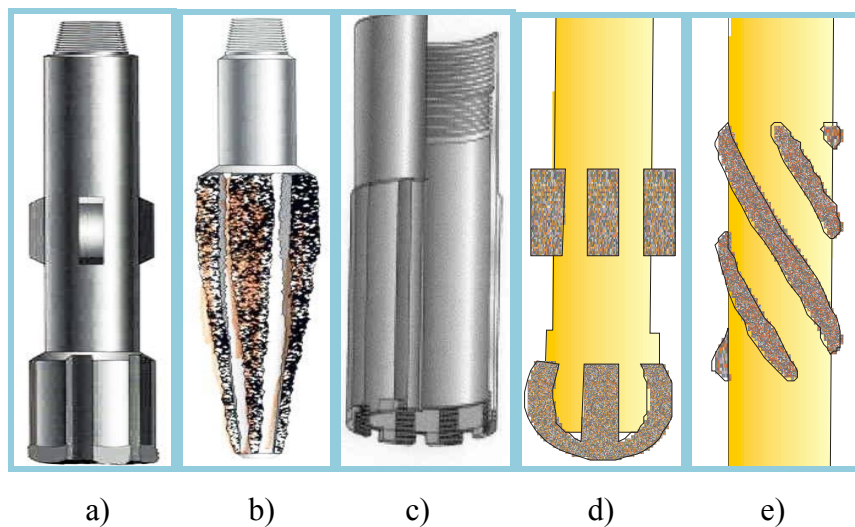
Herramientas de Limpieza y Fresado.
